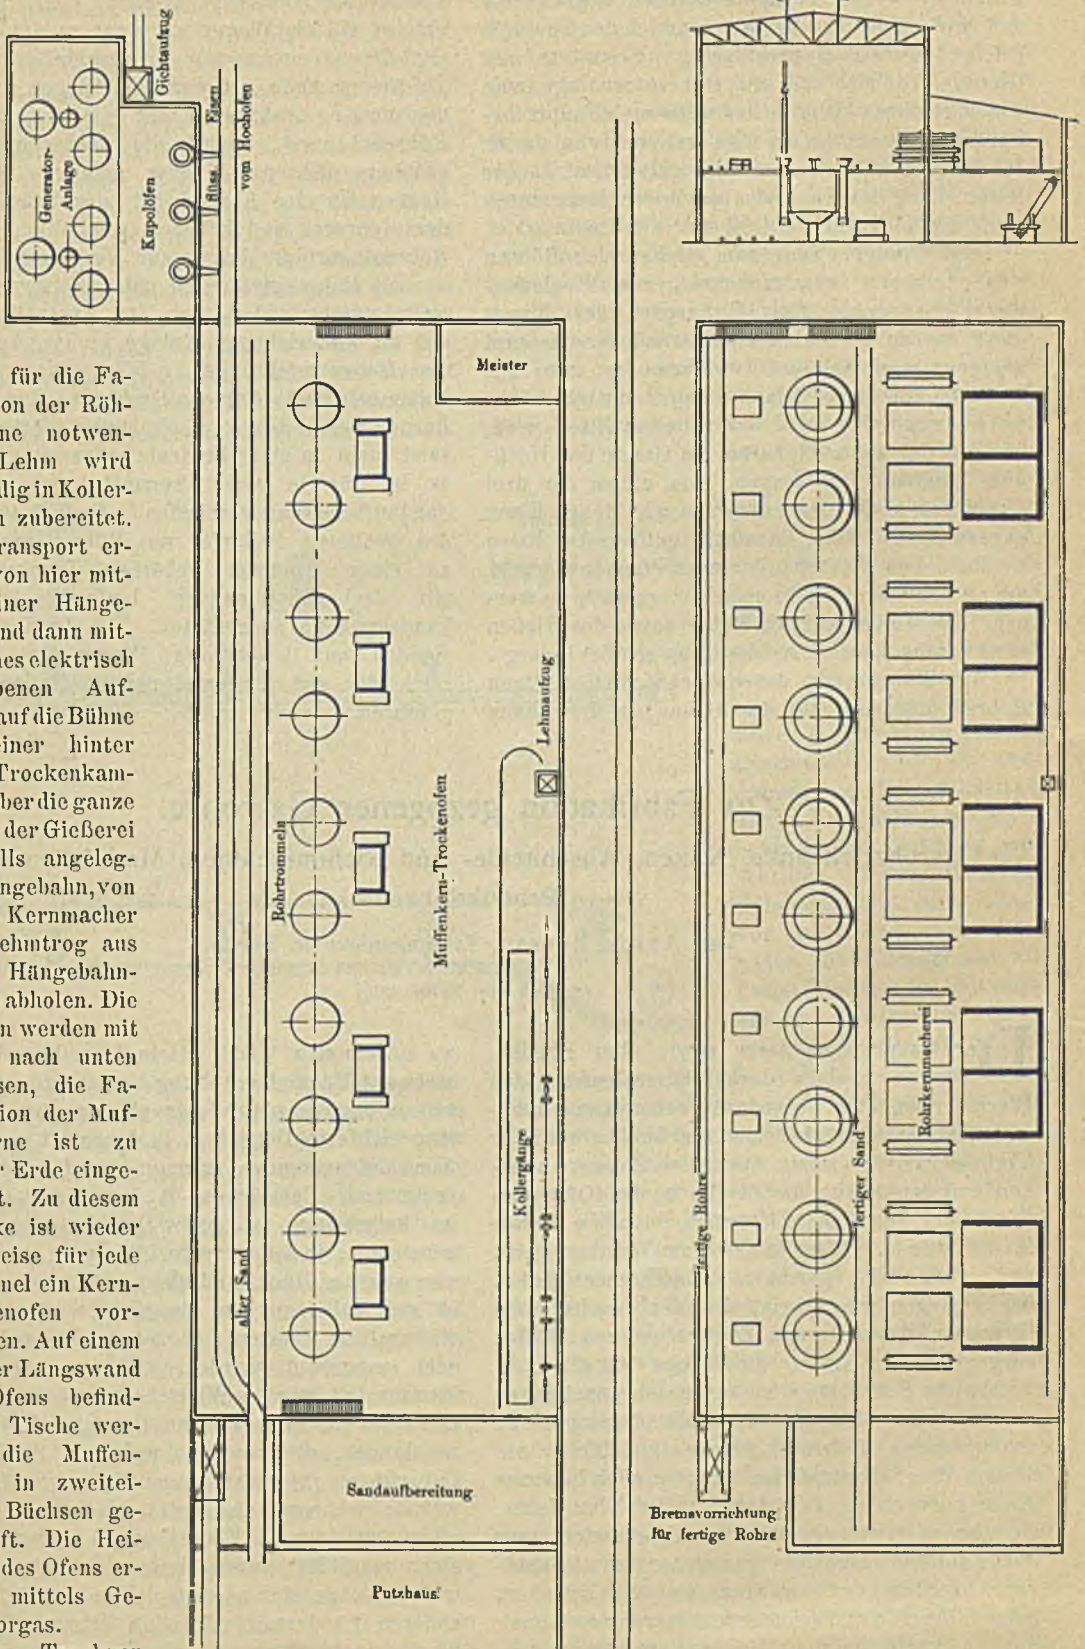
Lageplan einer Röhrengießerei mit 10 Blechtrommeln.
